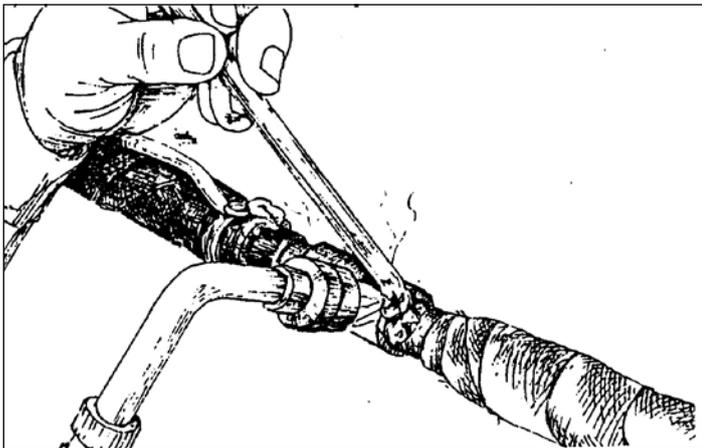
Припайка втулки к алюминиевой оболочке
